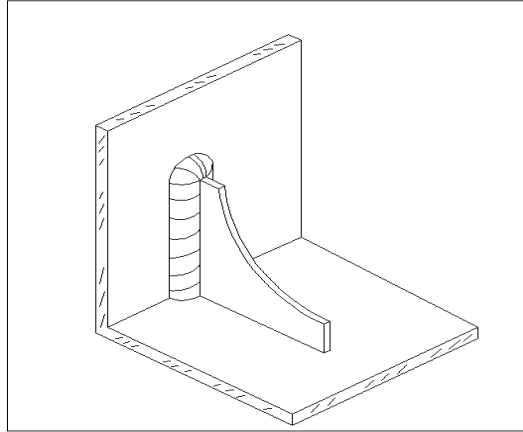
Detalle estructural soldado. Ref. [30]
